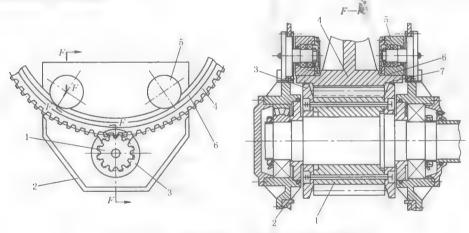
固定滚轮式 (BF型) 的悬挂安装结构 1—小齿轮; 2—传动架体; 3—辊子; 4—大齿轮; 5—滚轮; 6—内轨道; 7—外轨道
